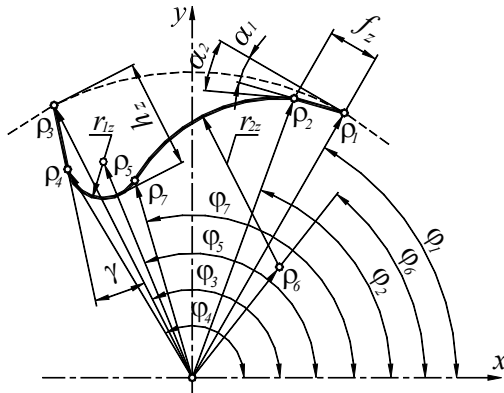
Схема розташування опорних точок профілю гвинтової канавки фрези
